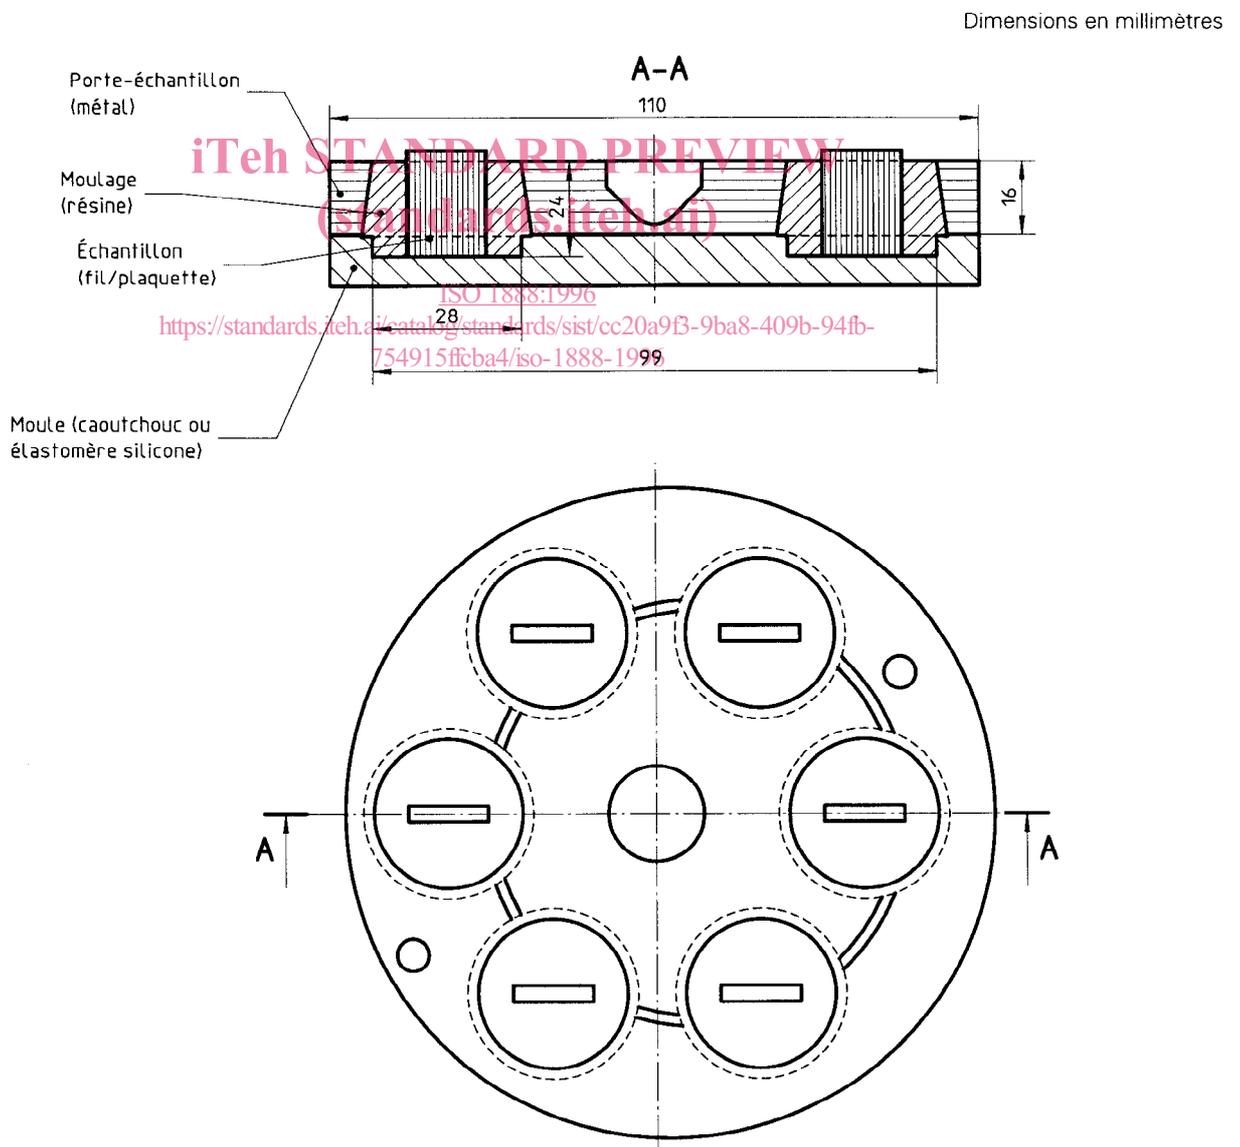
Exemple de dispositif pour mouler les éprouvettes
